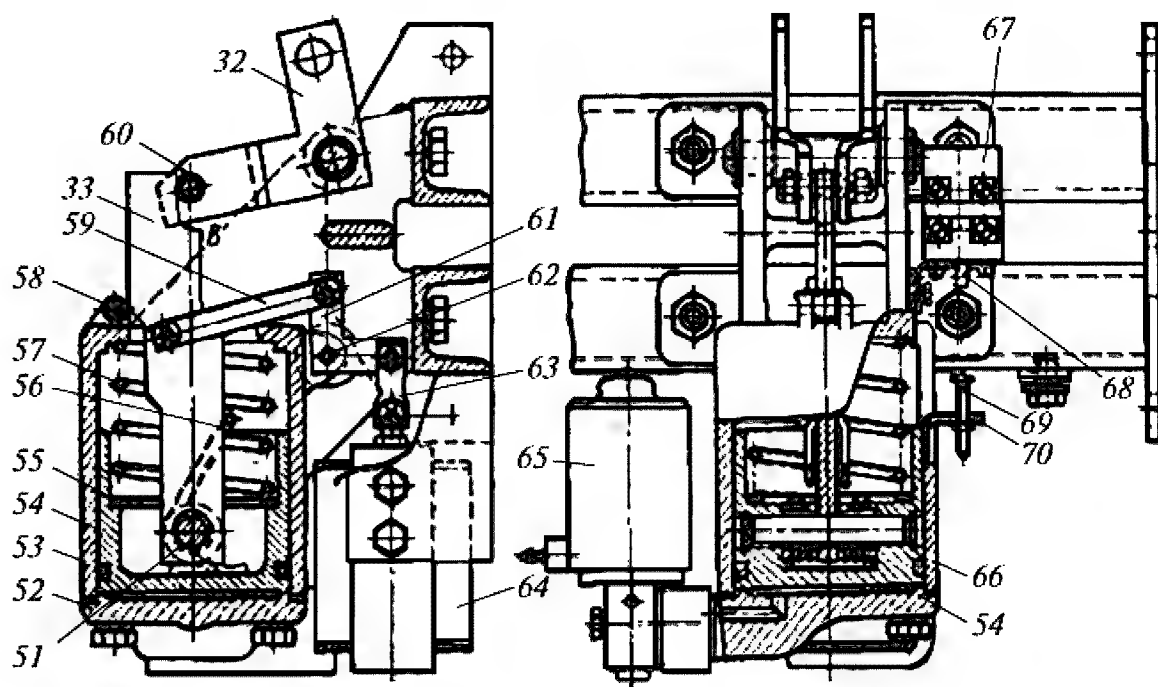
Пневматический привод быстродействующего выключателя 12НС
